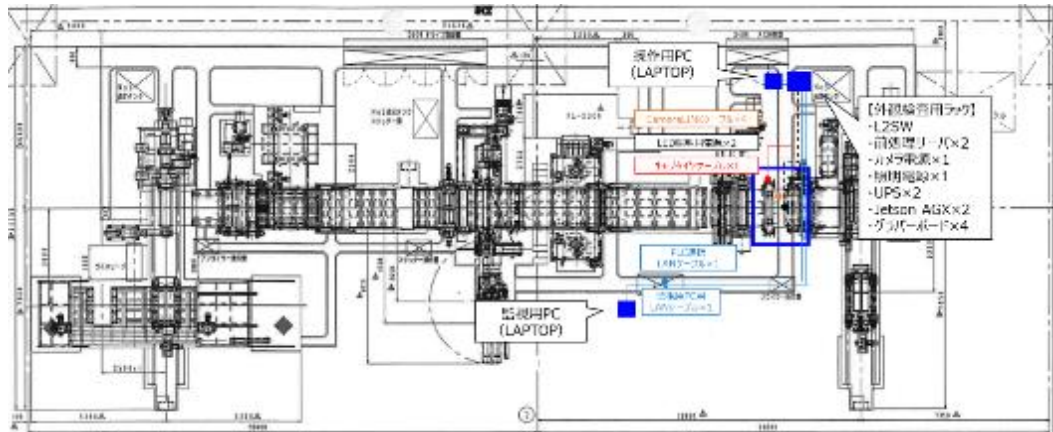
取り付け台座設置位置 (S2 平面図)
